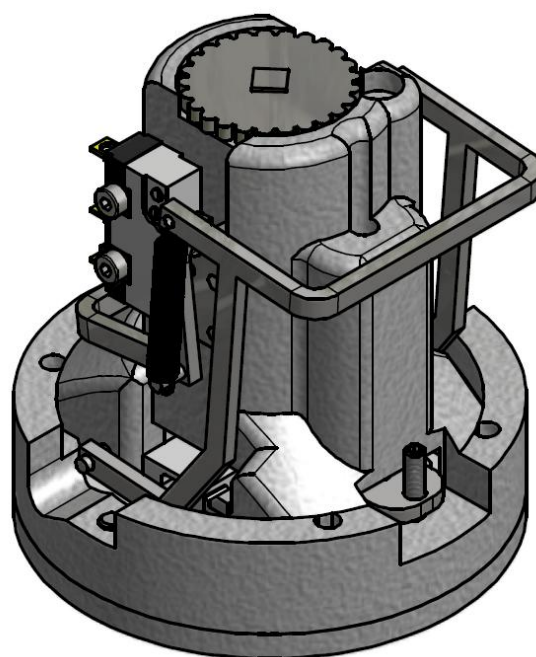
testované spínače APS 106, 116, 114 a 125
